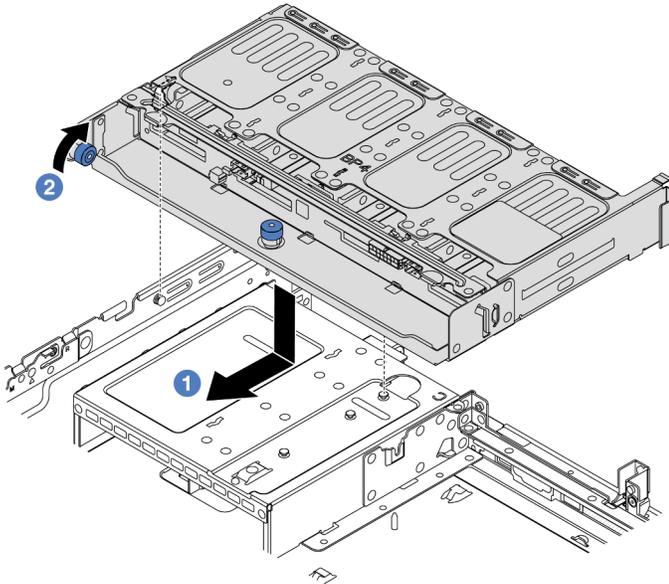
Installation du boîtier d'unités de disque dur arrière 8 x 2,5 pouces
